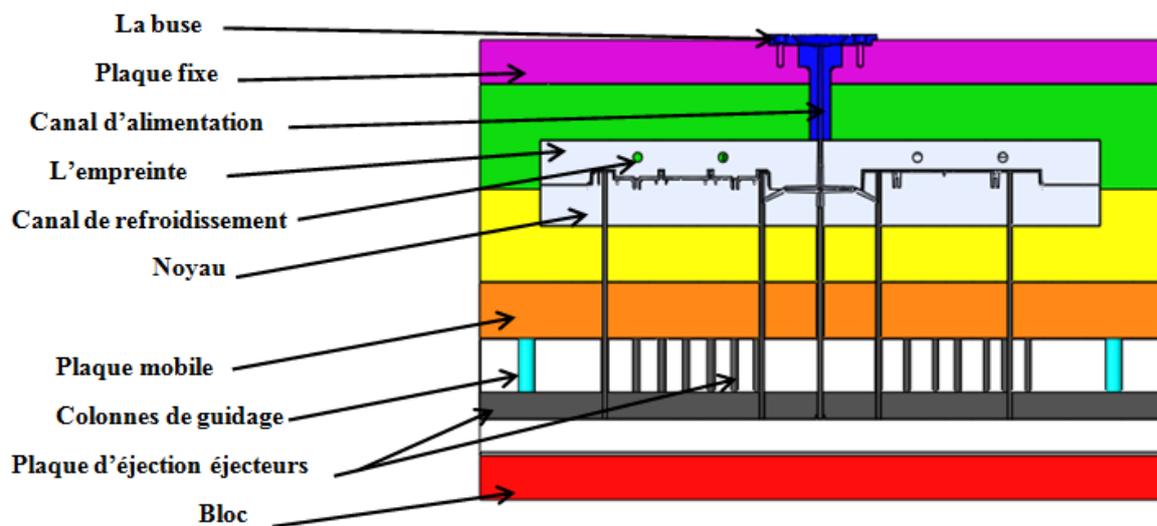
Moule pour la multi prise(vue en coupe).
